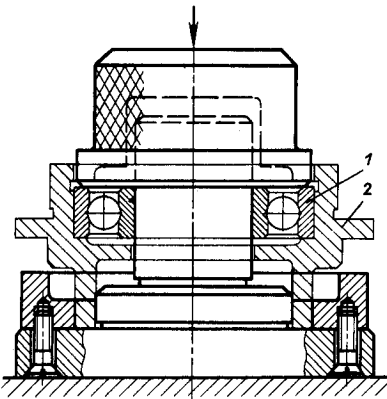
Базирование корпуса 2 и подшипника 1 при сборке
